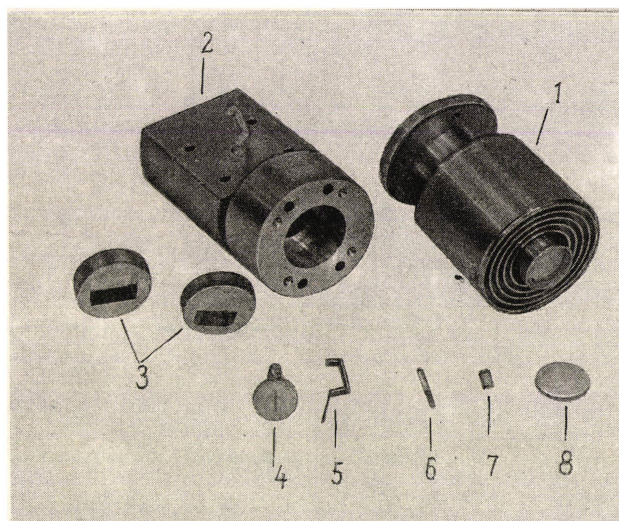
Детали конструкции блока облучателя с поляризатором (без преобразователя и канала звука):
